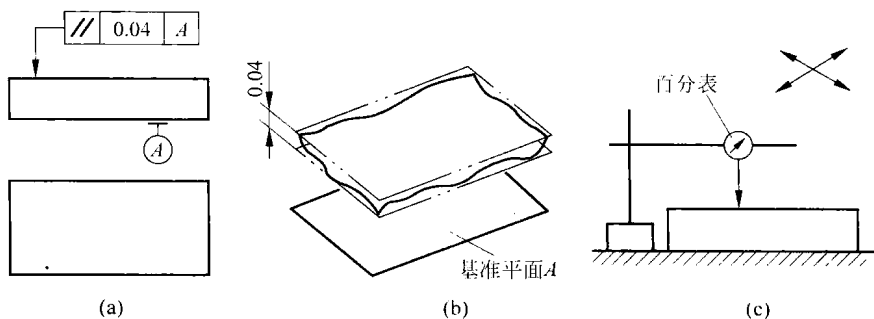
平行度公差的标注、公差带及检测方法
